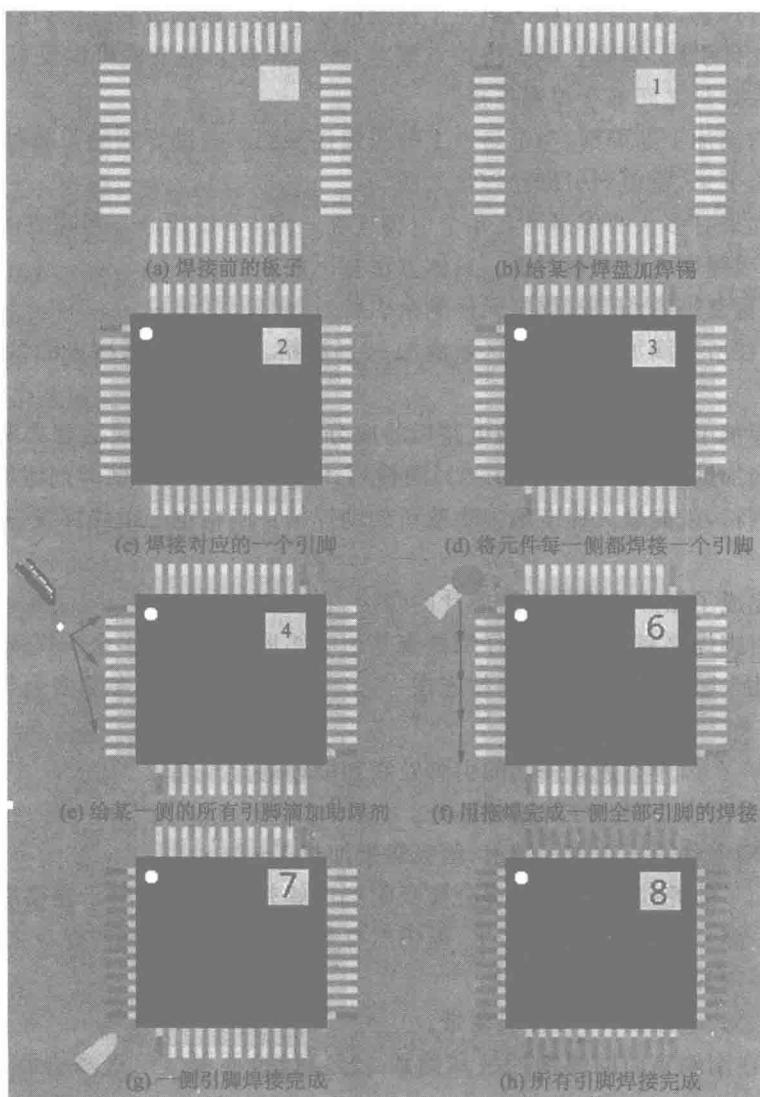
贴片式密集引脚芯片的焊接方法
